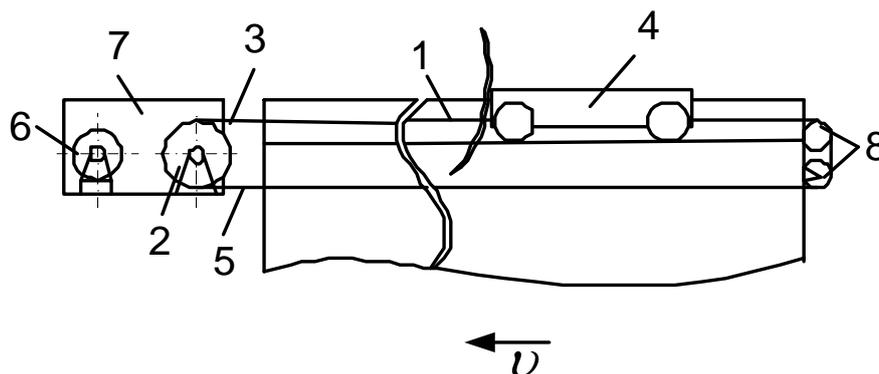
Схема запасовки канатов: 1 – канат; 2 – барабан; 3 – ветвь набегающая; 4 – тележка; 5 – ветвь сбегаящая; 6 – двигатель; 7 – коробка передач автомобильная; 8 – блоки неподвижные;  $v$  – направление рабочего движения
